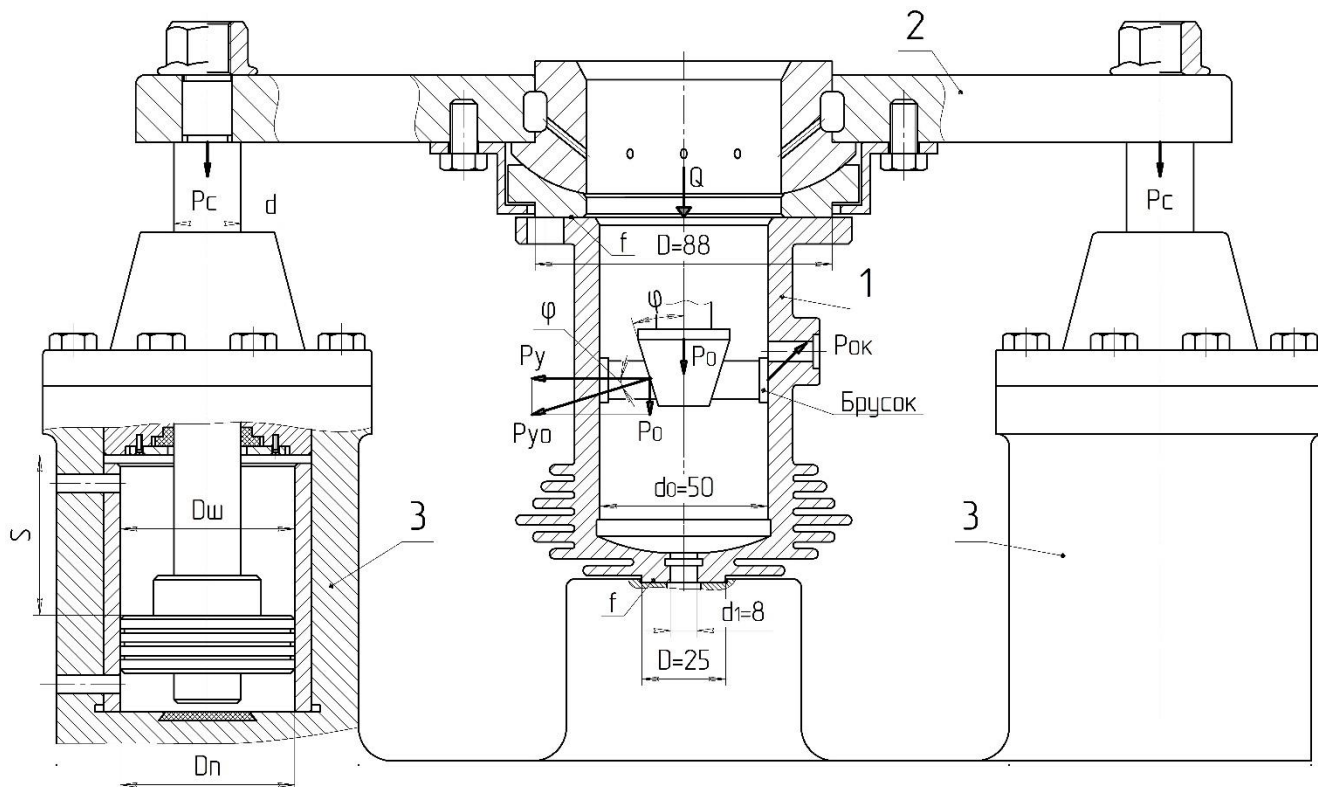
Схема затиснення заготовки по торцям та напрямок сил, що діють на брусок від механізму радіальної подачі хона
